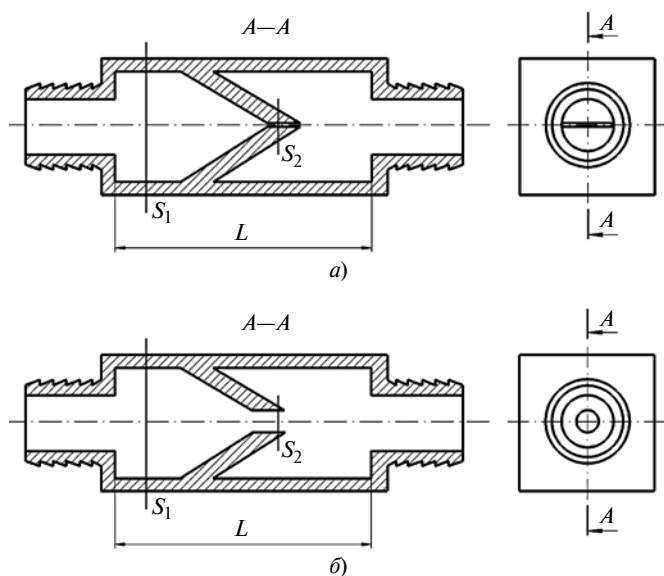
Гидродиоды с прямоугольным (а) и круглым (б) профилем поперечного сечения
